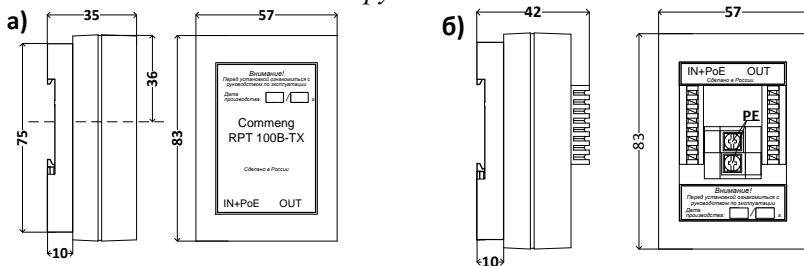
Габаритные размеры репитера Commeng RPT 100B-TX (а - с разъемами 8P8C (RJ-45), б - с врезными контактами idc)
